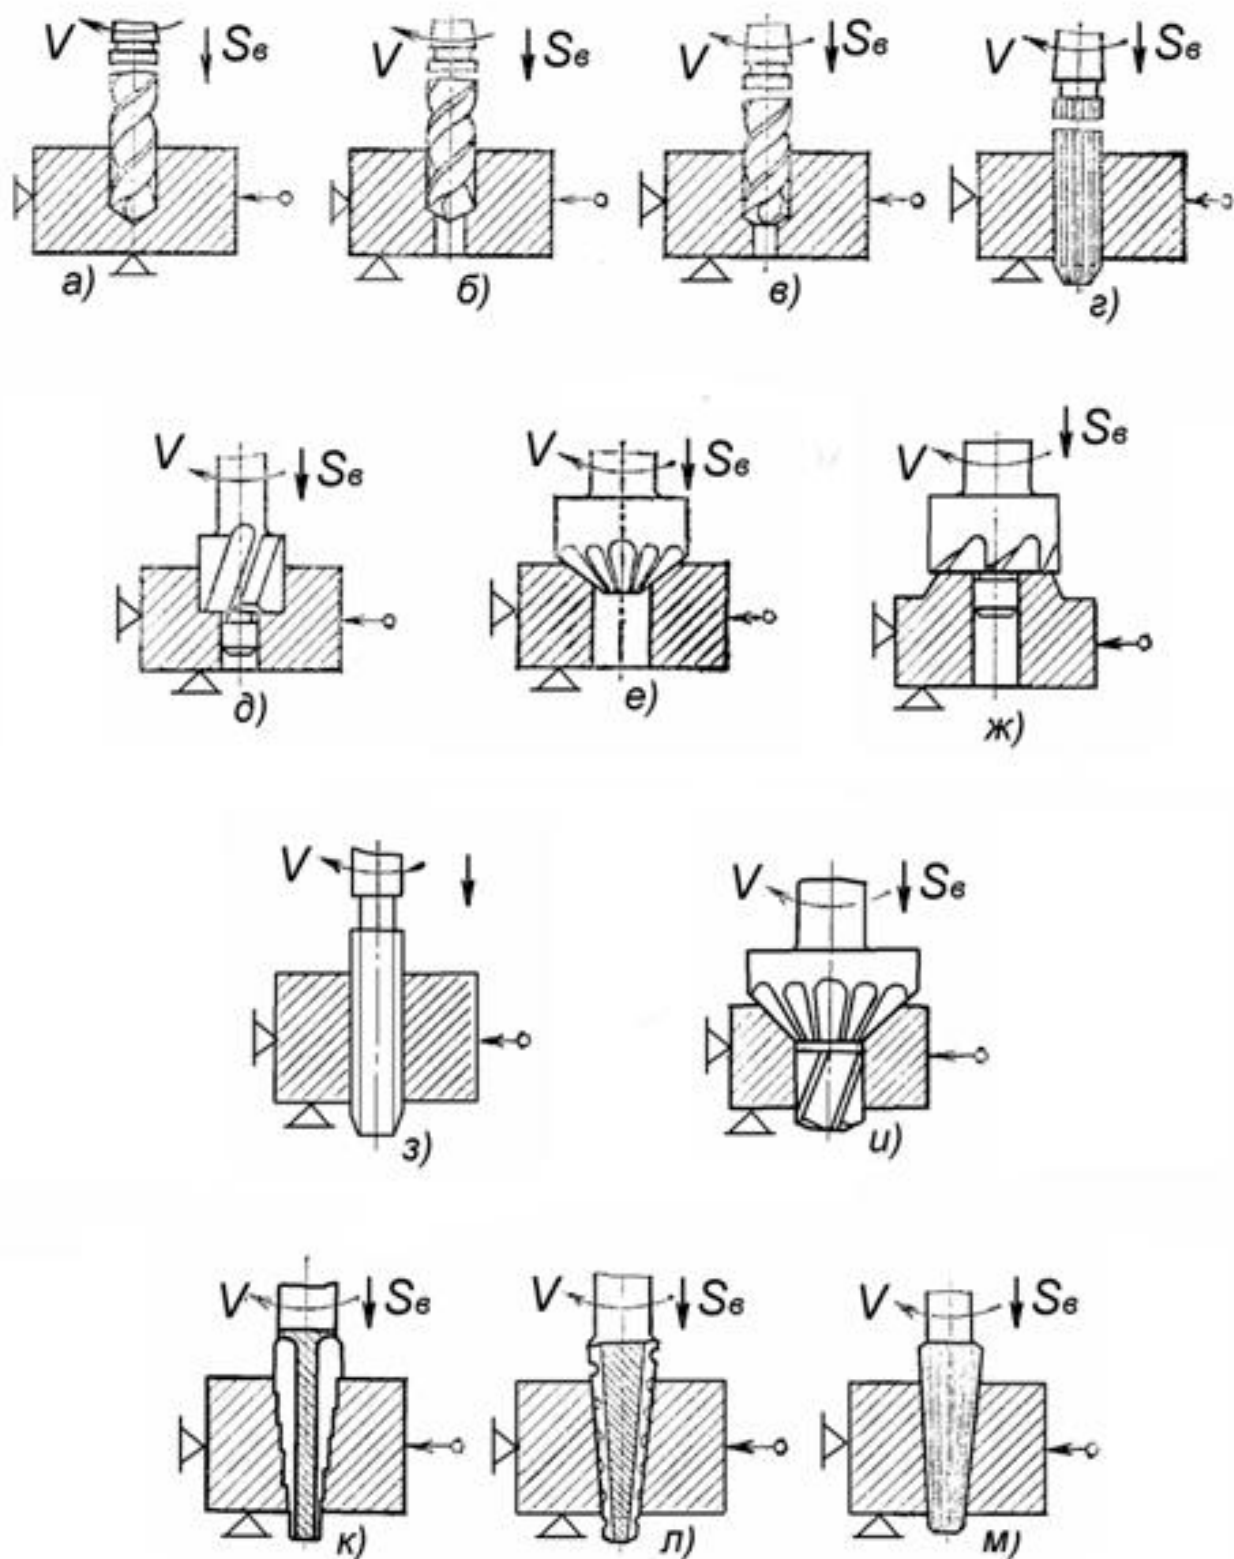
Виды обработки отверстий на сверлильных станках
